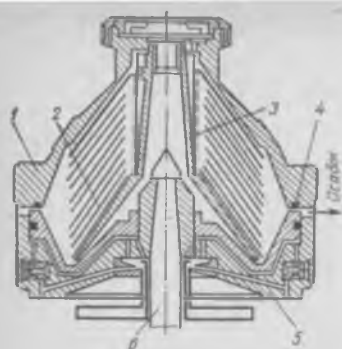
Схема барабана сепаратора-молокоочистителя:
